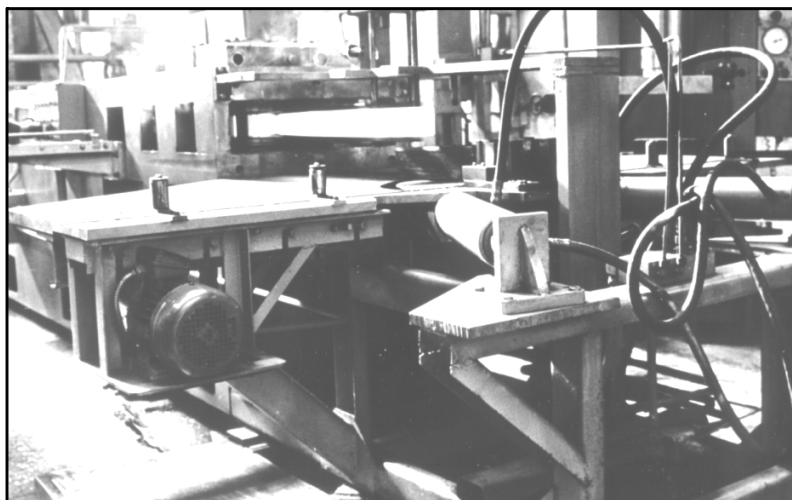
Прокатный стан в момент выхода двух прокатанных заготовок из клетки
